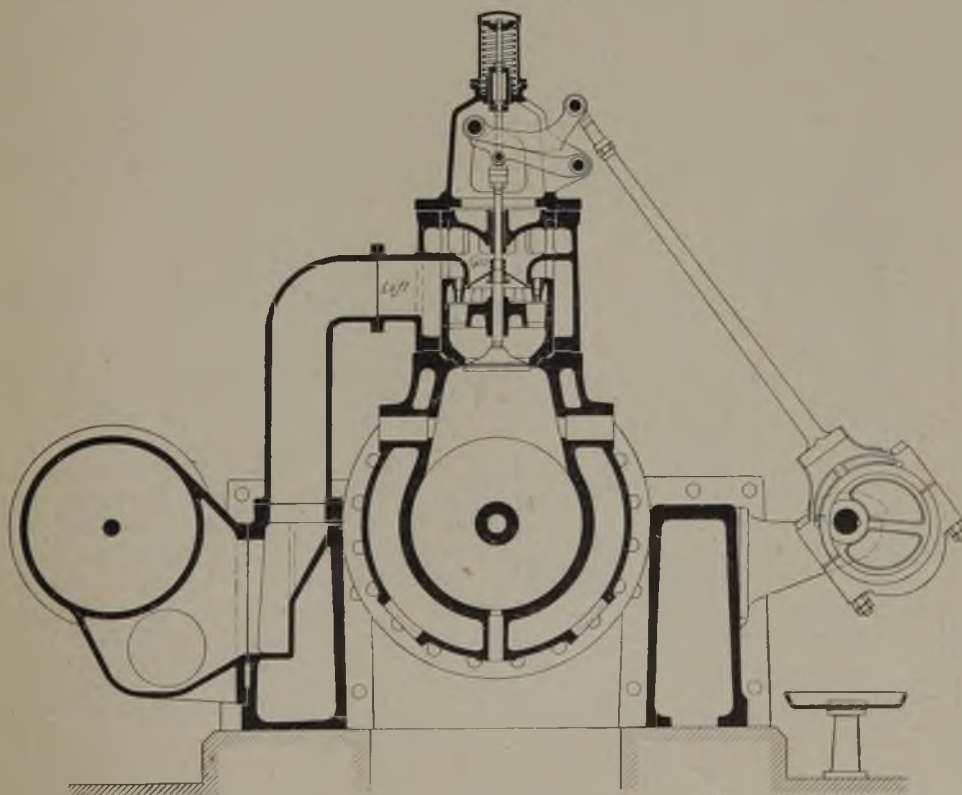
Querschnitt durch Einlaßventil und Steuerung der Gasmaschine.
